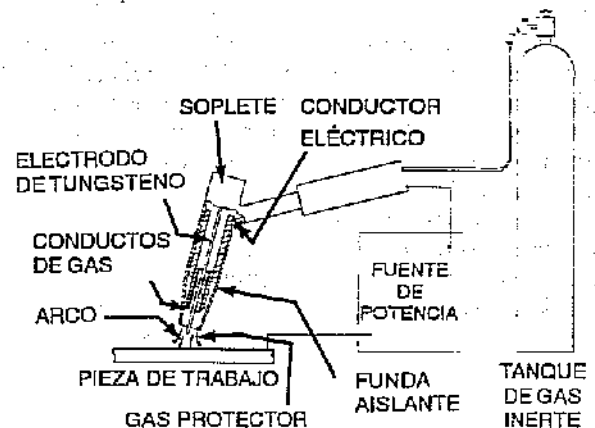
Disposición del equipo para soldadura por arco de tungsteno y gas
